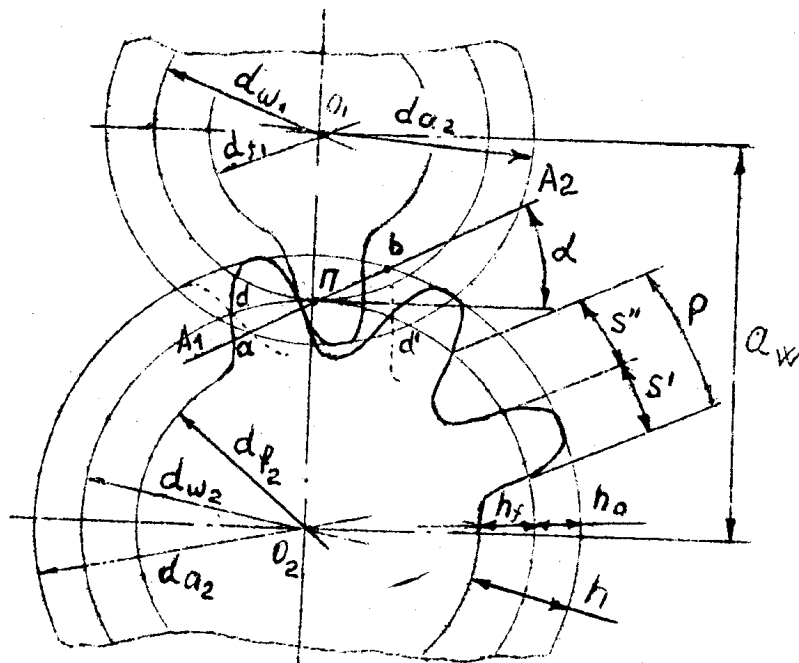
Схема цилиндрической передачи с прямыми зубьями
